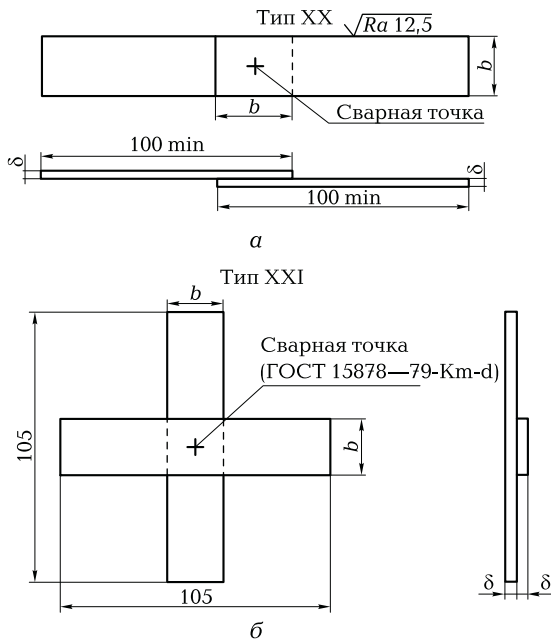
Образцы для механических испытаний контактной точечной сварки:
